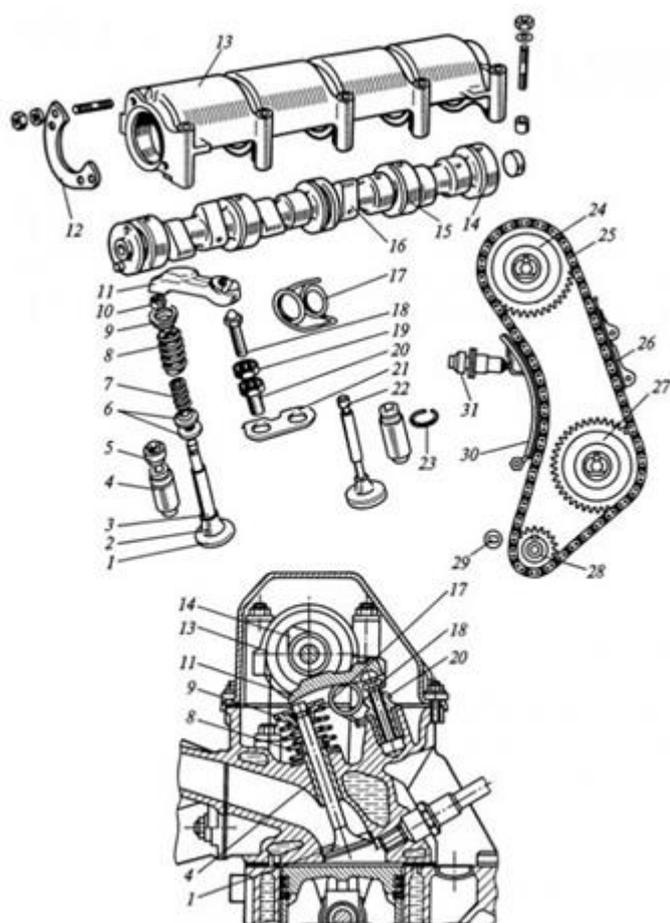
Газораспределительный механизм легкового автомобиля с цепным приводом. 1, 22 – клапаны; 2 – головка; 3 – стержень; 4, 20 – втулки; 5 – колпачок; 6 – шайбы; 7, 8, 17 – пружины; 9 – тарелка; 10 – сухарь; 11 – рычаг; 12 – фланец; 13 – корпус; 14 – распределительный вал; 15 – шейка; 16 – кулачок; 18 – болт; 19 – гайка; 21 – пластина; 23 – кольцо; 24, 27, 28 – звездочки; 25 – цепь; 26 – успокоитель; 29 – палец; 30 – башмак; 31 – натяжное устройство
